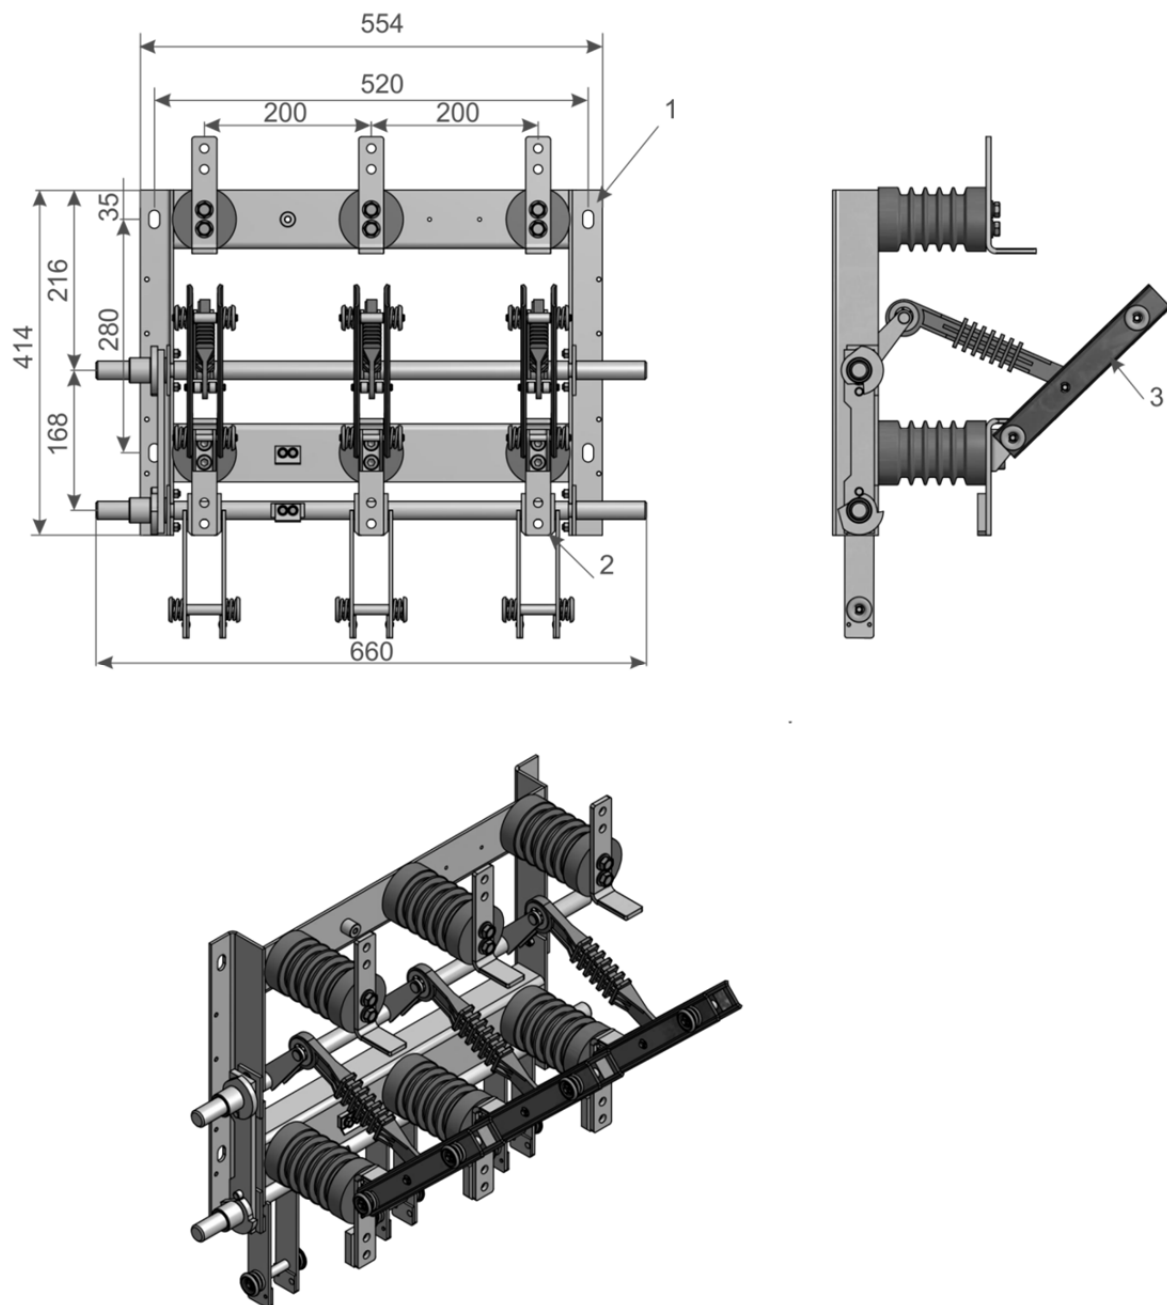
Габаритно-установочные размеры и устройство разъединителя РВЗ
